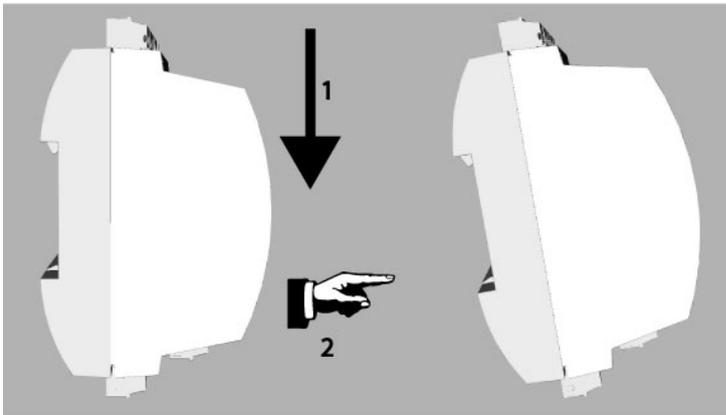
Desmontaje del AMC2 del carril de montaje
